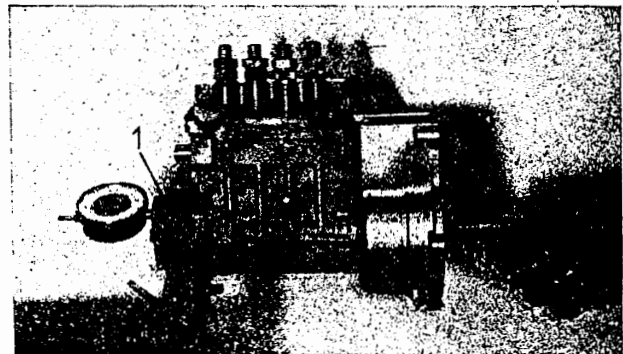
Axiales Spiel der Nockenwelle mit Meßvorrichtung (Werkzeug Nr. W 89) prüfen (1)
